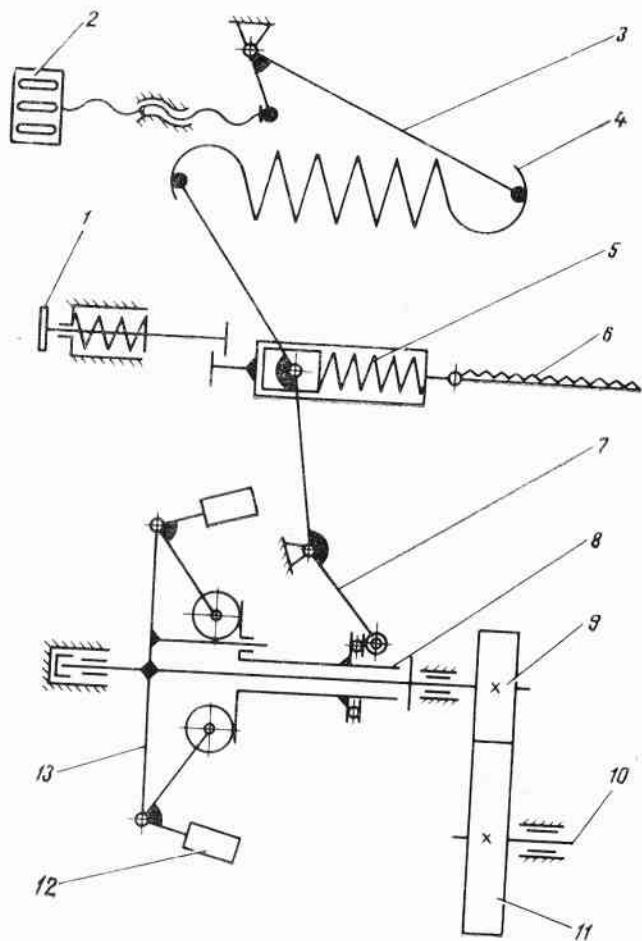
Кинематическая схема центробежного однорежимного регулятора:
